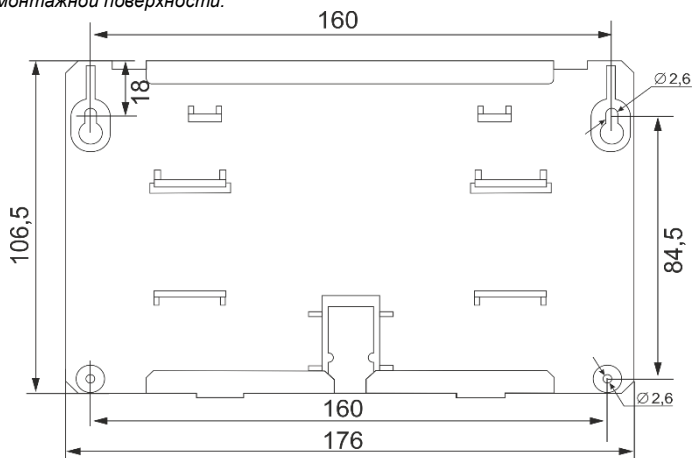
Установочный эскиз основания корпуса RS485/FTTx-S-SC
